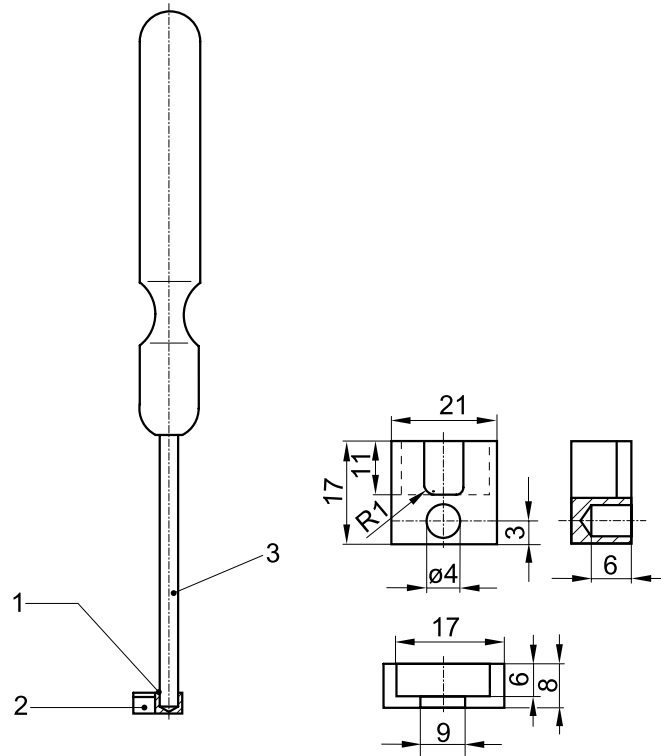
Werkzeug zum Einstecken der Kabelstecker an den Magnetspulen
